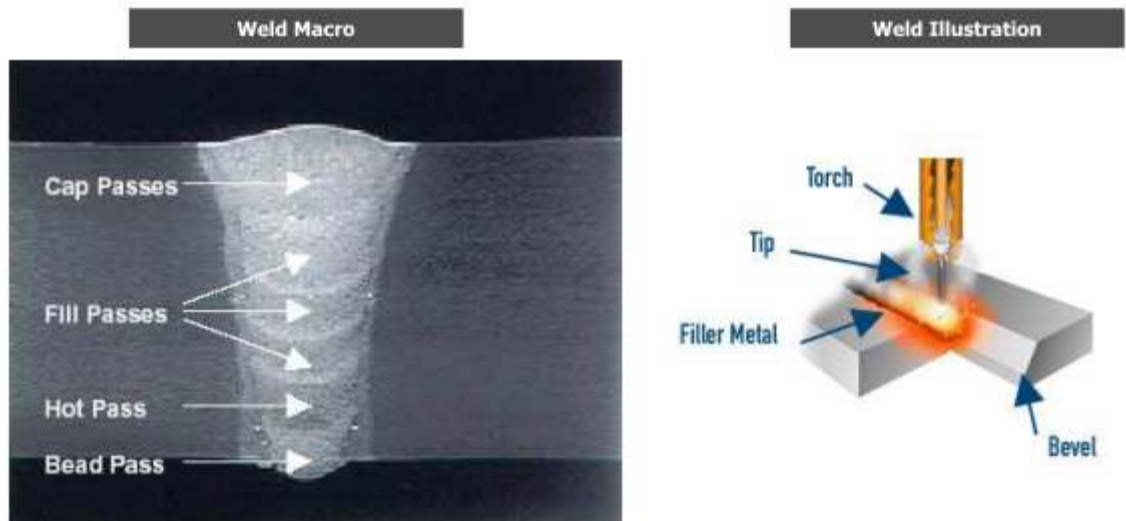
Ilustración de la macro gráfica del cordón de soldadura finalizado. LINCOLN ELECTRIC: Sistemas de Automatización en Procesos de Soldadura, Presentación, (2011). p. 4
